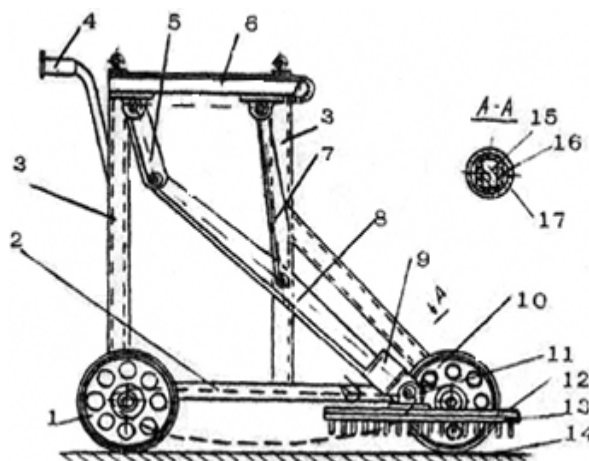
Схема компоновки устройства для очистки плоских поверхностей
